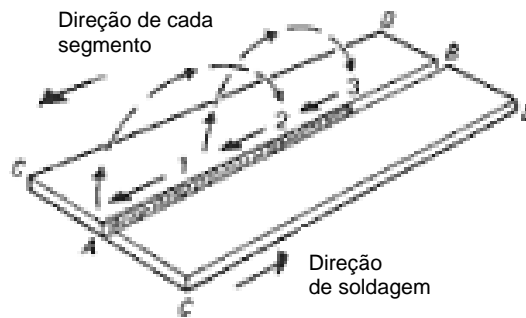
Soldagem com passe-a-ré (AWS, 2001).
